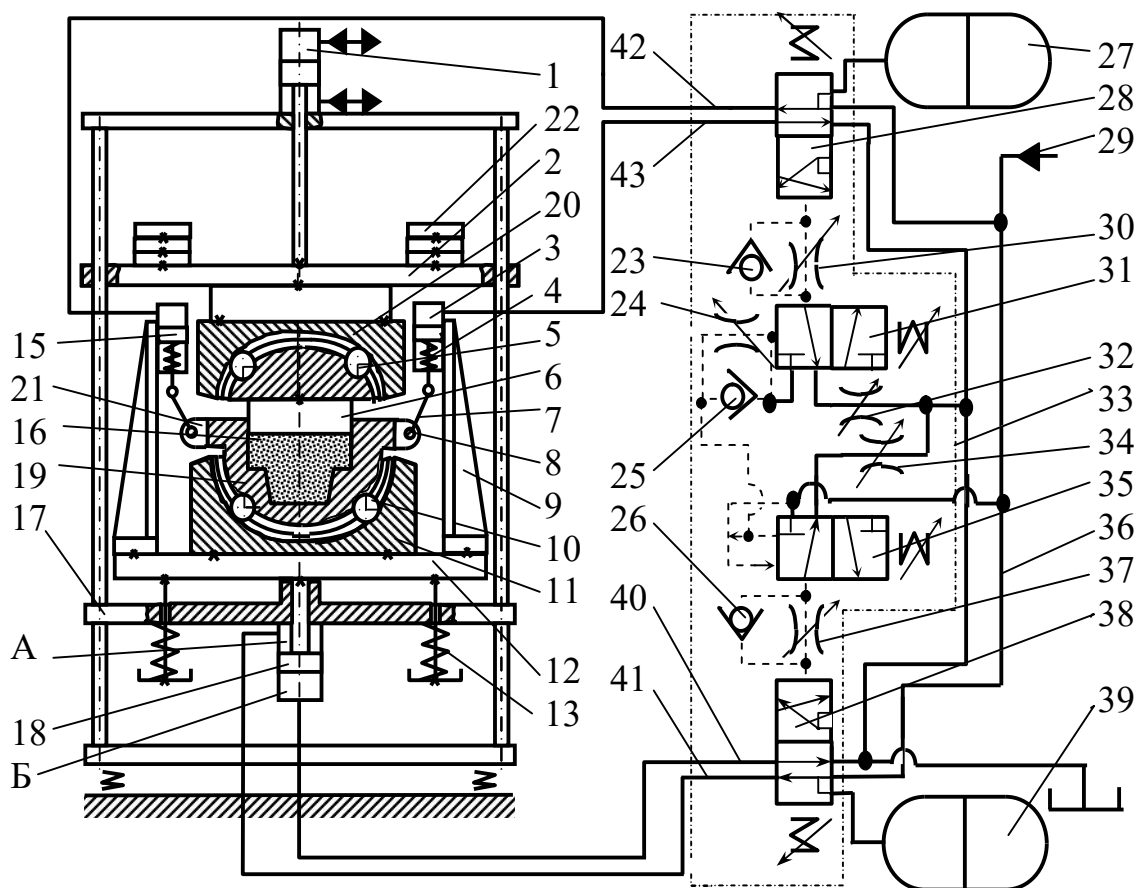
Конструктивна схема вібропреса для БКВН на базі ІВПМ з додатковим горизонтальним зворотно-поворотним рухом прес-форми
